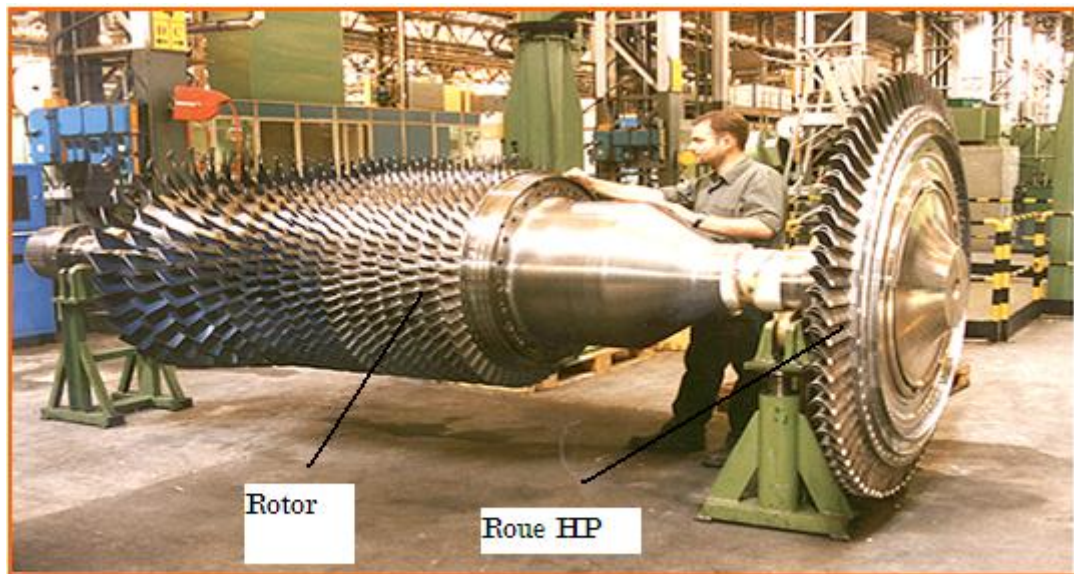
Rotor du Compresseur de la turbine à gaz MS
